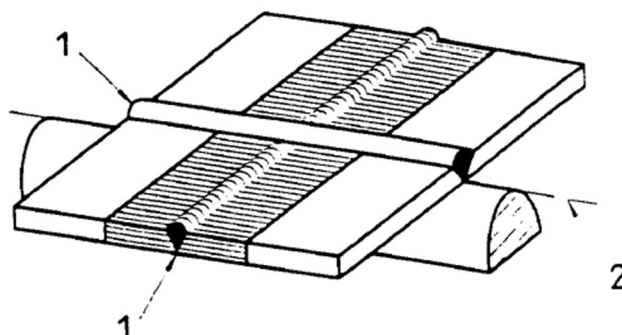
Zkušební vzorek rovinného výrobku s tupým svarem [37]
